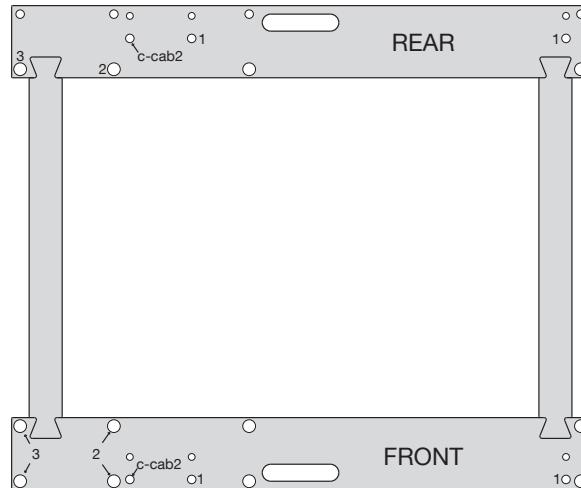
Draufsicht auf die montierte Bohrschablone
